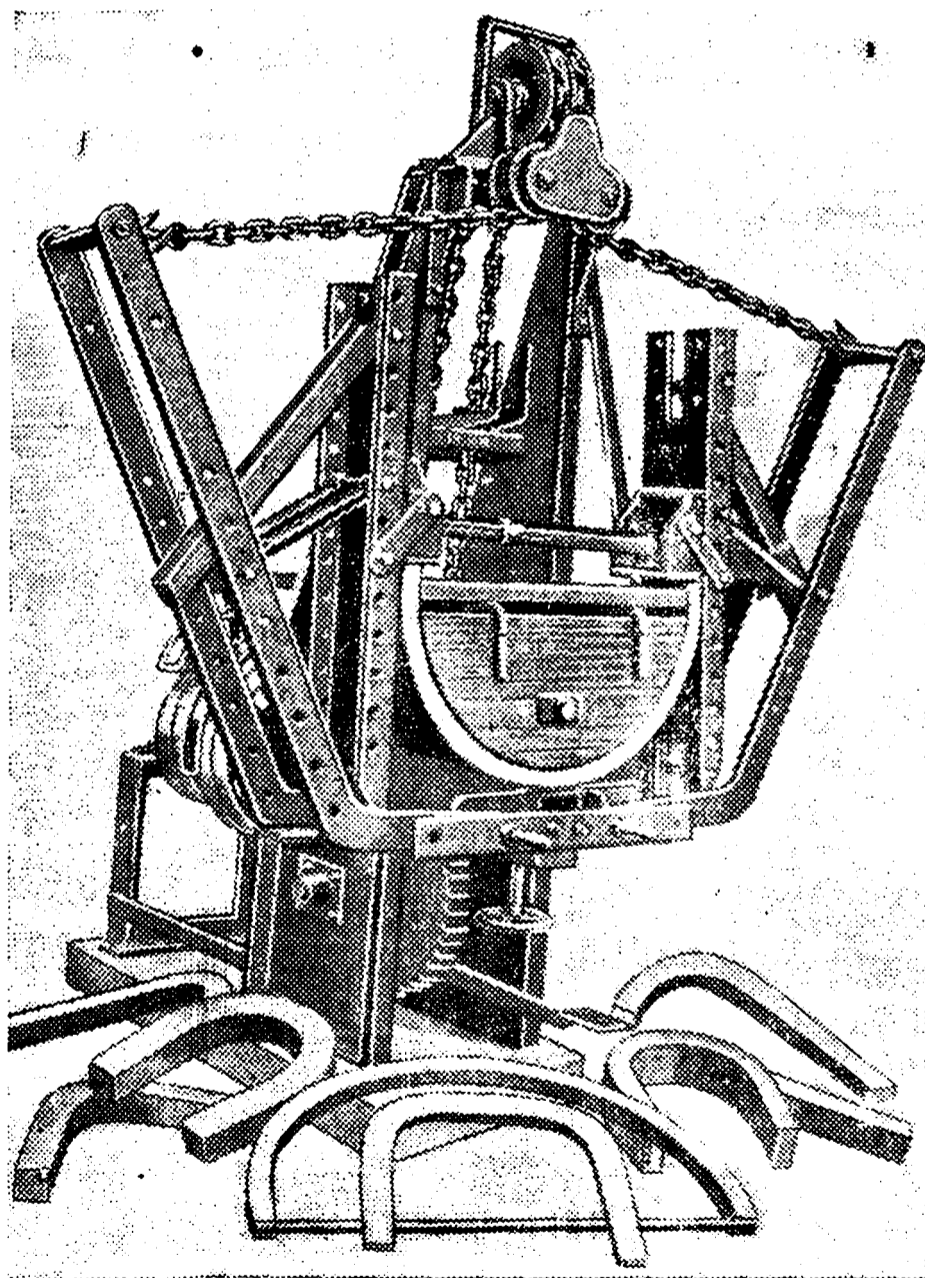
Станок для гнутья деталей с незамкнутыми контурами
